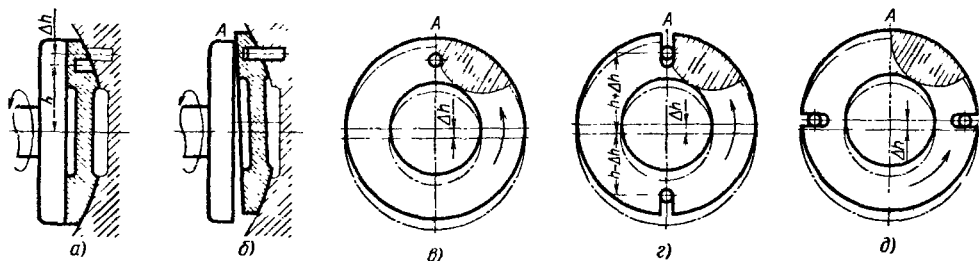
Схема образования масляного клина в подшипниках со сферической опорой
